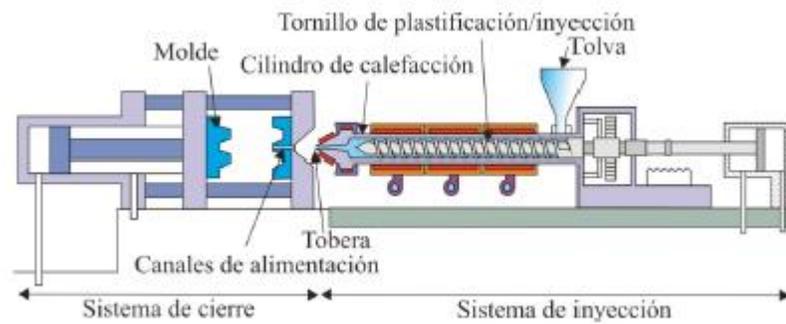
Máquina de moldeo de husillo (Beltrán Rico & Marcilla Gomis, 2012)
